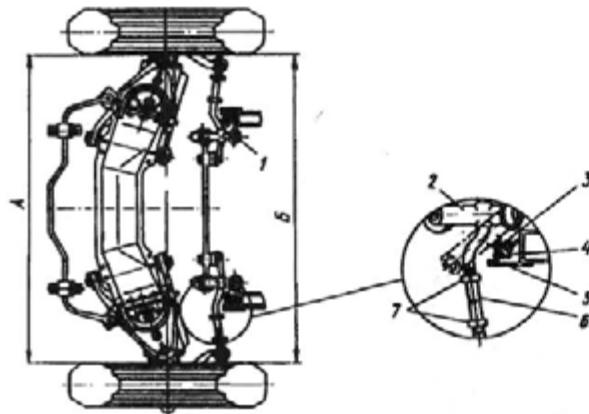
Установка переднего колеса для регулировки схождения телескопической линейкой и максимального угла поворота:
